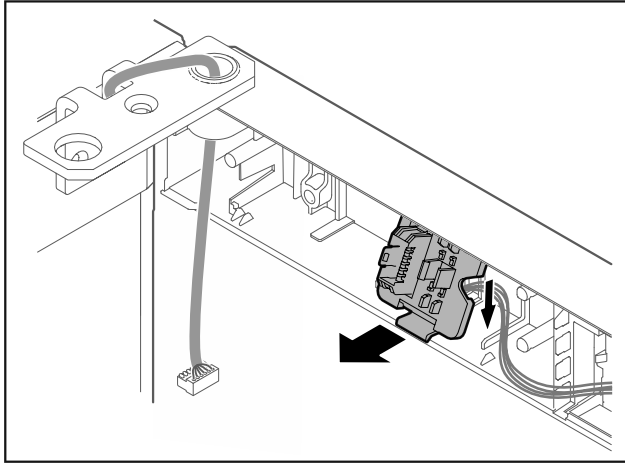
La posición de montaje del soporte del conector puede estar girada 180°.
